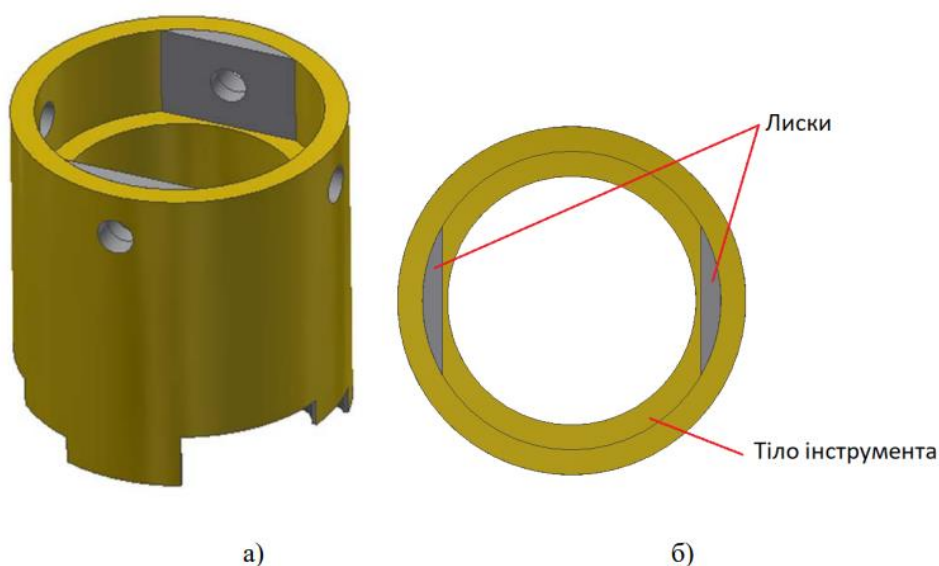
Лиски (а – аксонометрія, б – вид зверху) [17]
